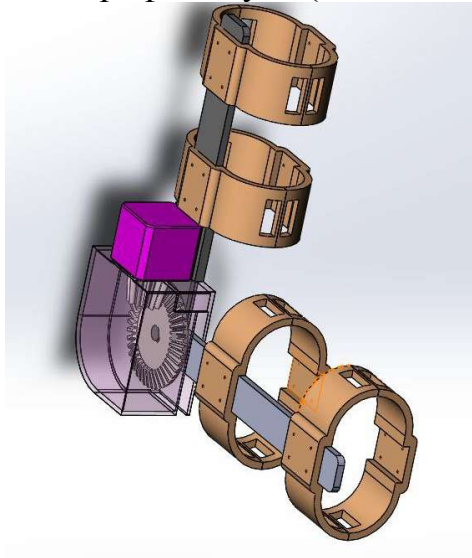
Ортез ліктьового суглобу Рис 9.17. Конічна зубчаста передача
